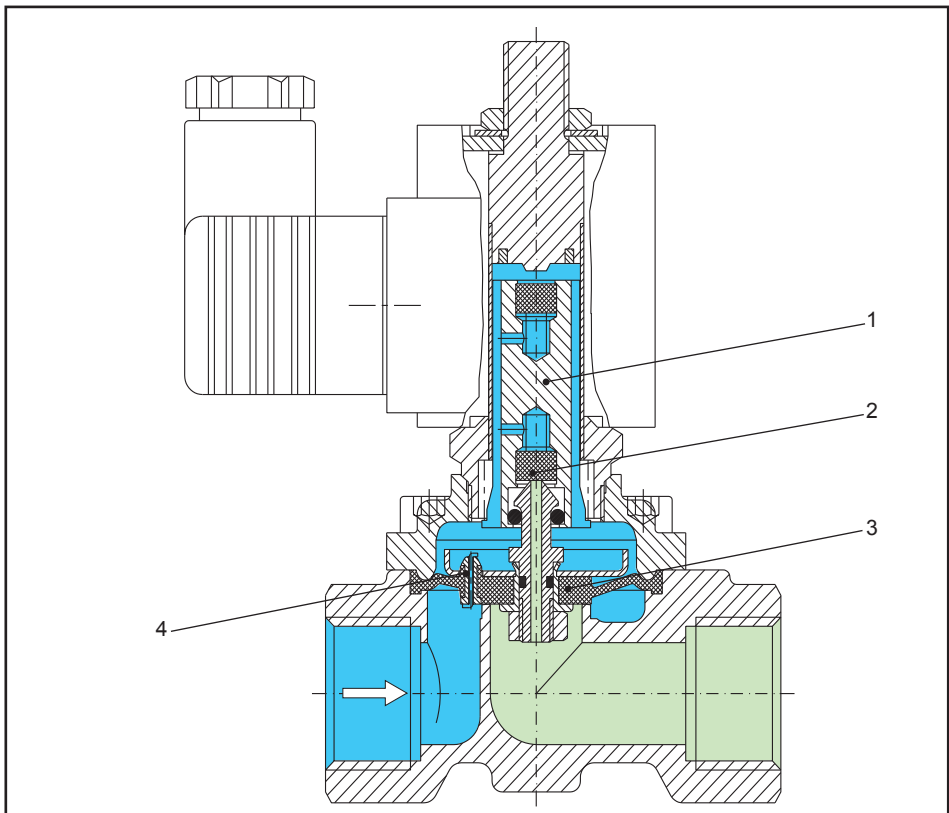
Zwangsgesteuertes Magnetventil: Standard- Ausführung
